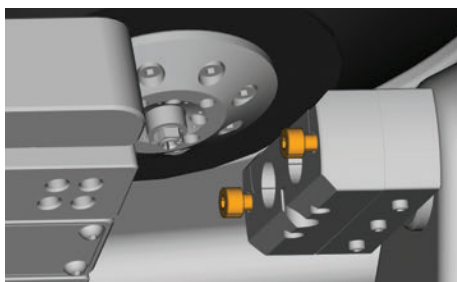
FIJACIÓN DEL SOPORTE DE PILARES PREFACE®
